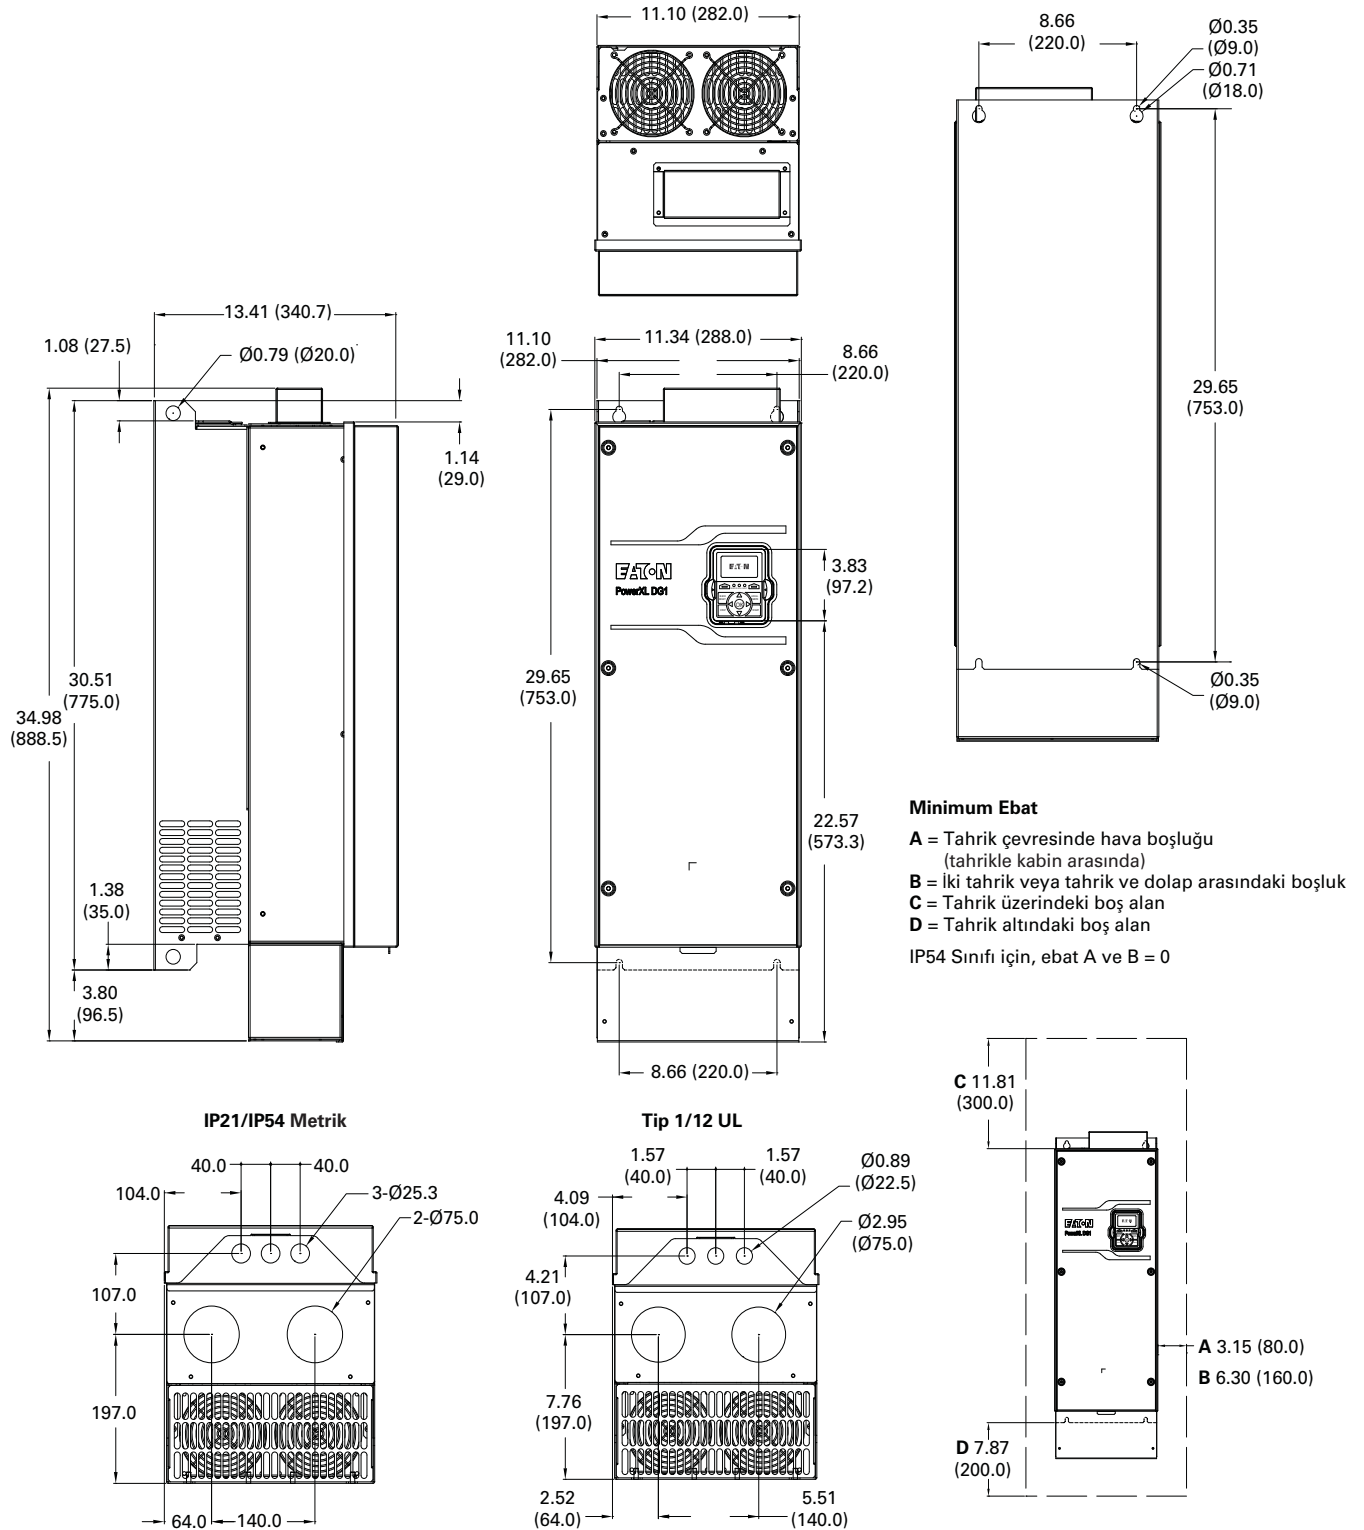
FR4 Boyut Çizimi Flanş Montajı
